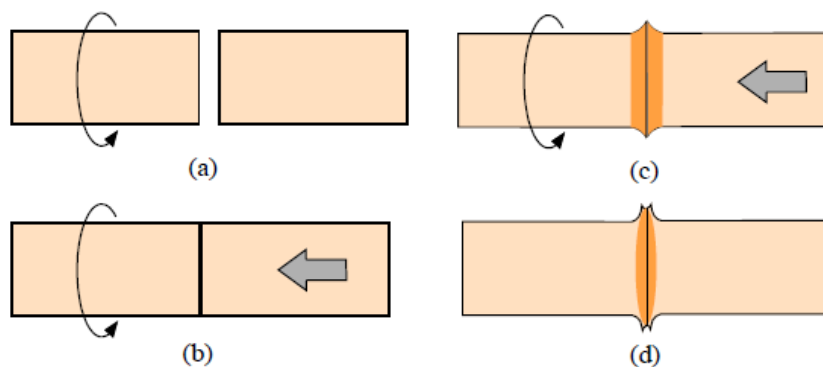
Estágios da soldagem por atrito: (a) Um membro é colocado em rotação, (b) inicia-se a força de compressão, (c) inicia-se a formação da solda e (d) a solda é completada (MODENESI 2001).
